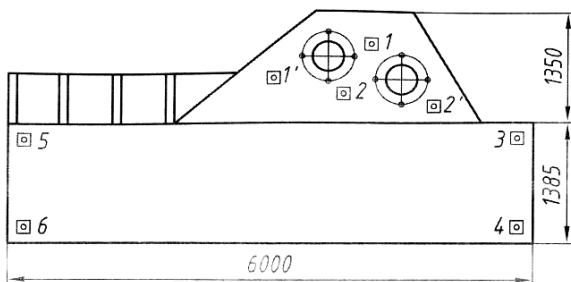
Схема розташування датчиків на корпусі вибивної машини
